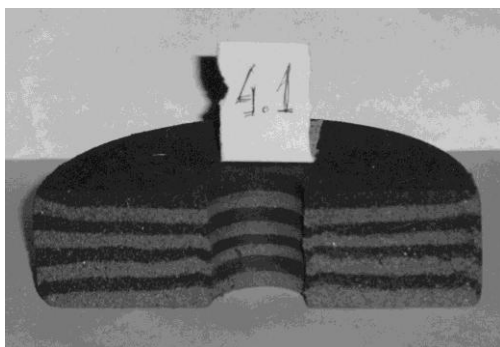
Заготовка абразивного круга после прессования из двойной заготовки с переворотом
